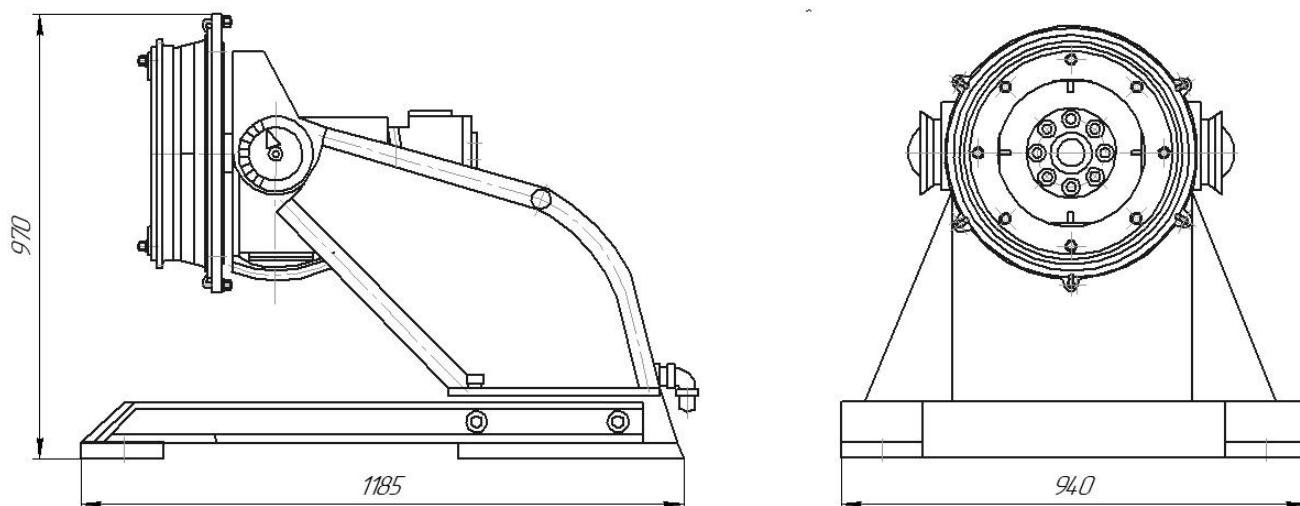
Зварювальний маніпулятор HD-50
